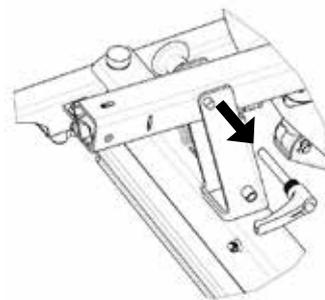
Zoom sur la poignée de serrage du mât dévissée
